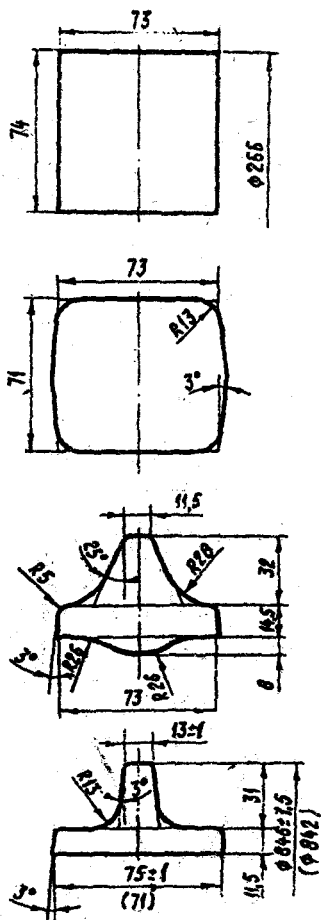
Калибровка заготовки кольца компрессора из сплава ХН45МВТЮБ
